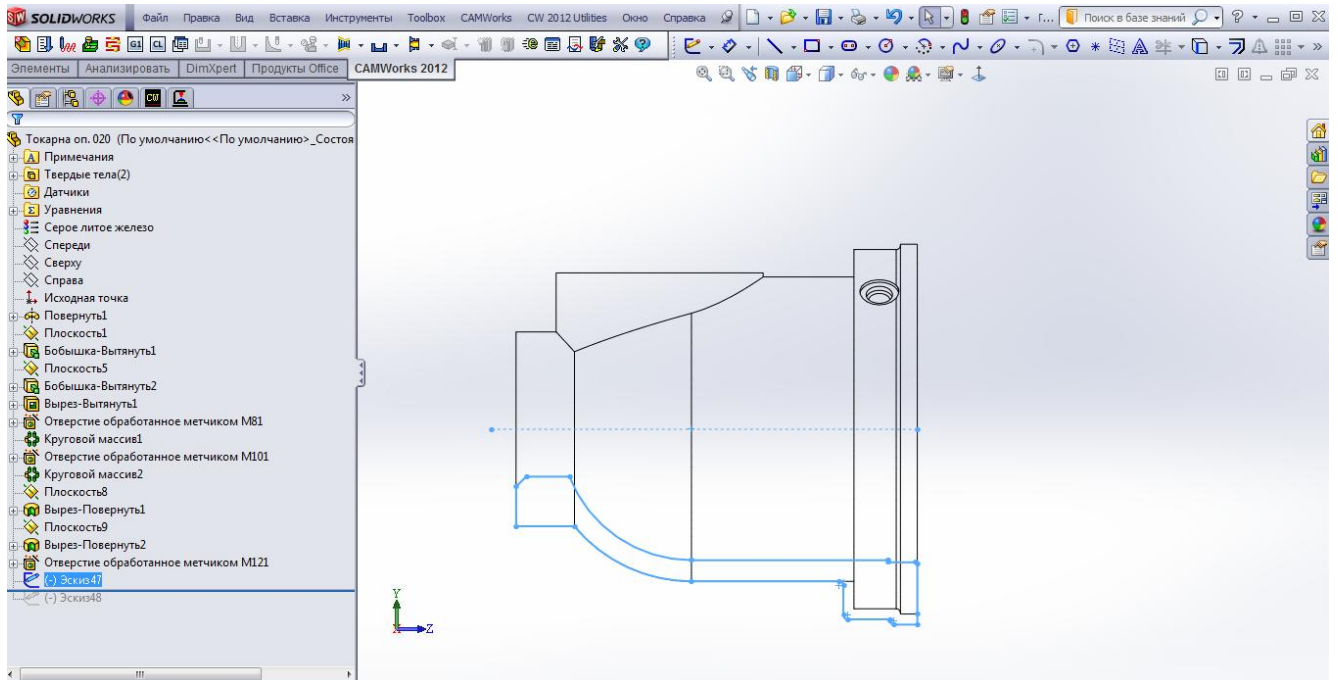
Побудова додаткового ескізу для визначення заготовки.
